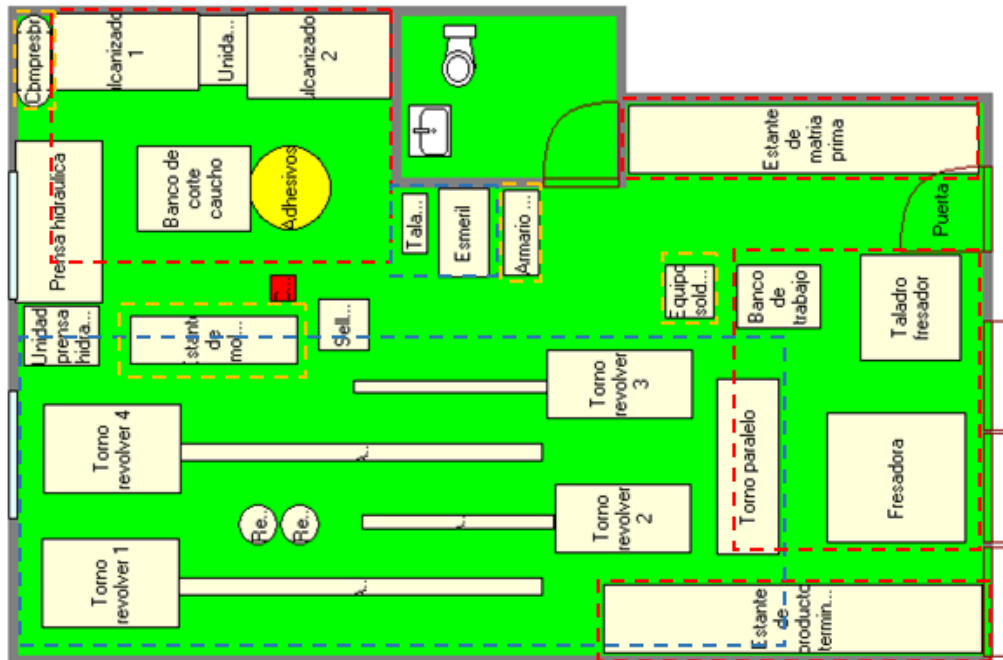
Propuesta B de Layout de la planta de manufactura de autopartes. Fuente: Propia
